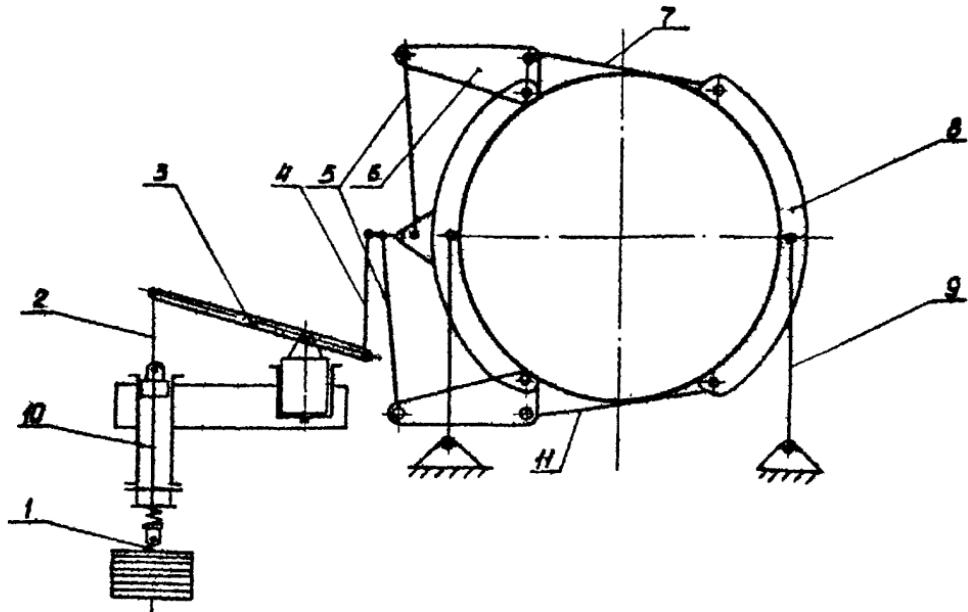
Тормоз с комбинированным приводом (рабочий - пневматический, предохранительный - пневмогрузовой) подъемных машин НМО и НМД: 1 - тяга грузов ; 2 - Штанга ; 3 - дифференциальный рычаг ; 4,5 - вертикальная тяга ; 6 - угловой рычаг ; 7,11 - горизонтальная тяга ; 8 - тормозная балка ; 9 - стойка ; 10 - шток.
